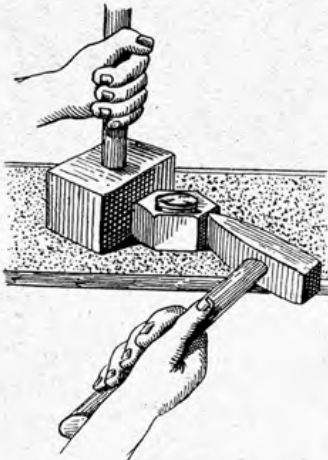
Lösen stark eingefressener Schraubenmuttern. Text auf dieser Seite.
